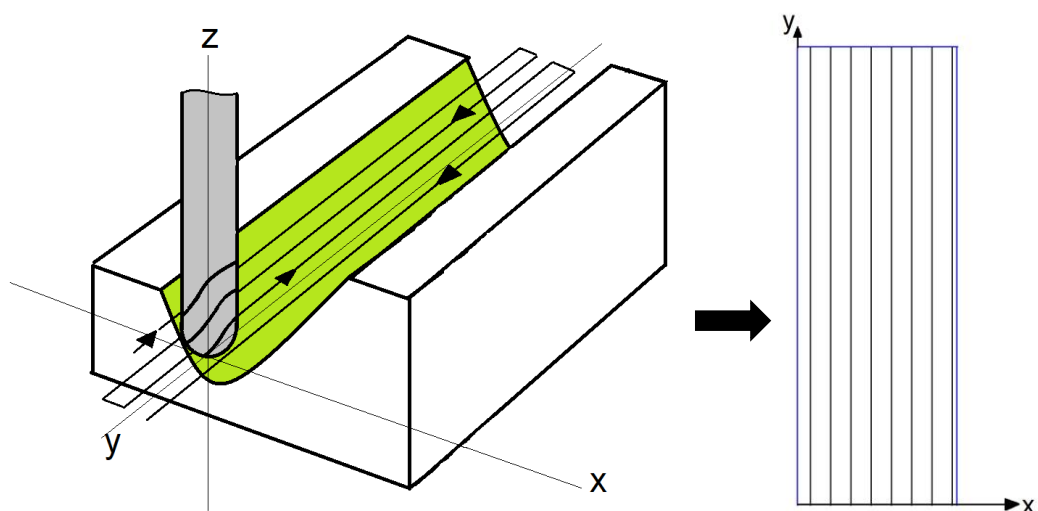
Схема фрезерования с траекторией, расположенной вдоль формообразующей поверхности
